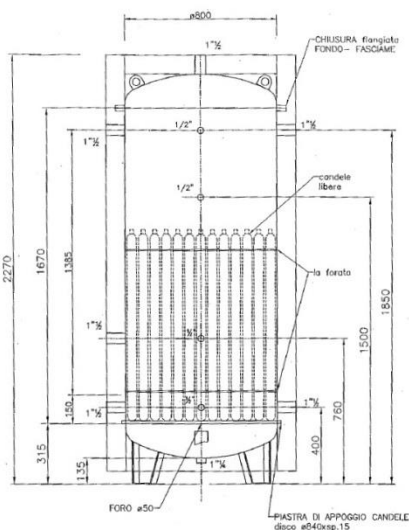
Accumulo PCM, vista in sezione e disposizione dei tubi all'interno dell'accumulo.
